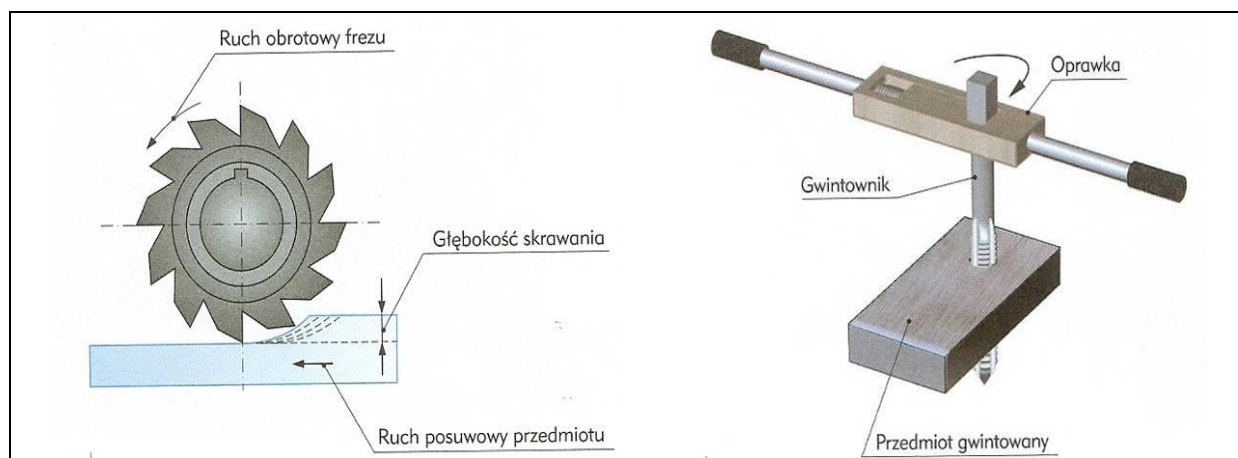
Opis podstawowych sposobów obróbki skrawaniem
